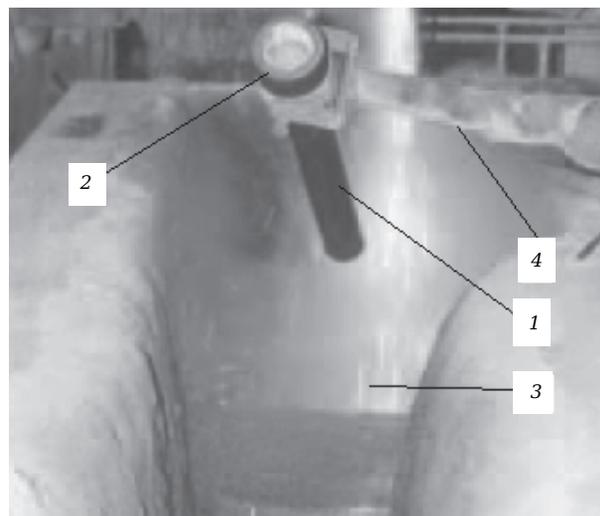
Установка манипулятором защитной трубы сталеразливочного ковша в промежуточном ковше: 1 — защитная труба; 2 — уплотнительное устройство; 3 — приемная камера промежуточного ковша; 4 — манипулятор
